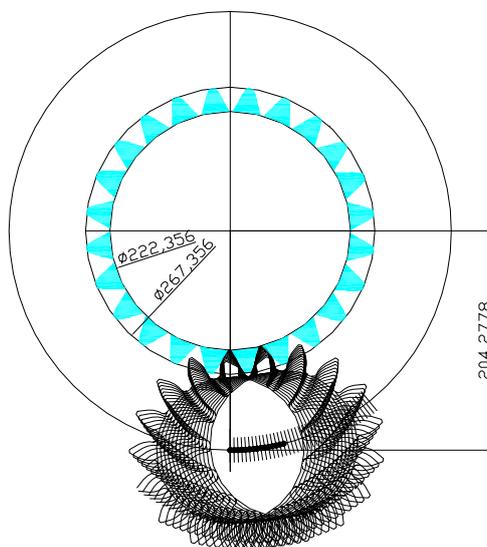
Положения долбяка относительно неподвижной заготовки и построение всех зубьев колеса
